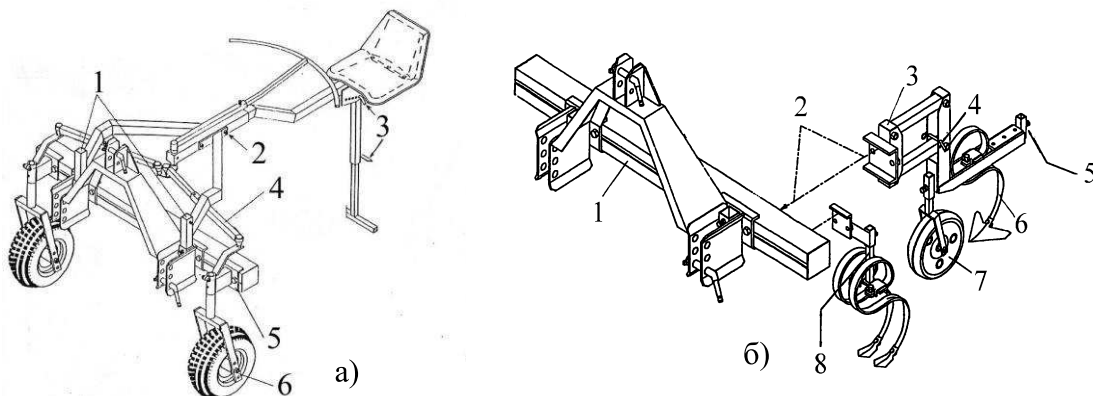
Культиватор ГС «Egedal»: а – рама культиватора: 1 – место установки секций; 2 – рулевой механизм; 3 – сидение оператора; 4 – регулируемые тяги; 5 – механизм регулировки колес; 6 – управляемые колеса с механизмом регулировки; б – рабочая секция культиватора: 1 – рама культиватора; 2 – место соединения рабочей секции и поперечного бруса; 3 – копирующая рельеф местности рабочая секция; 4 – блокировочный штифт; 5 – место крепления рабочих органов; 6 – универсальная лапа; 7 – копирующее колесо рабочей секции; 8 – рабочие элементы
